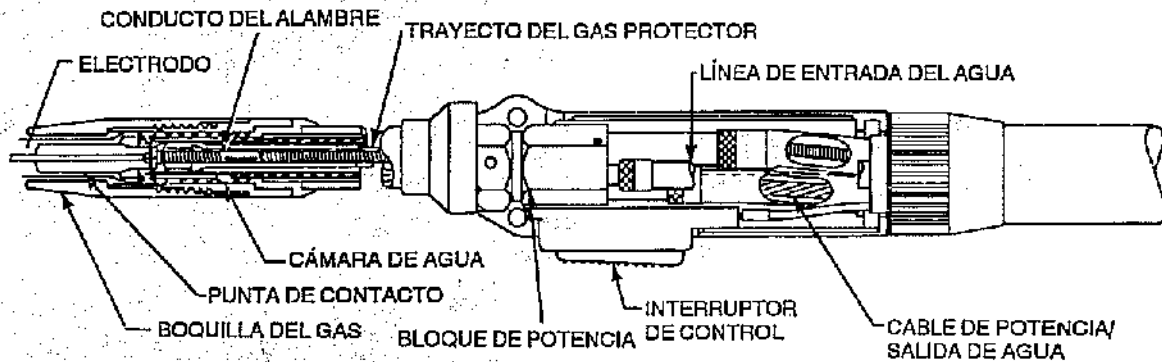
Vista en corte seccional de una pistola para soldadura por arco de tungsteno y gas típica
